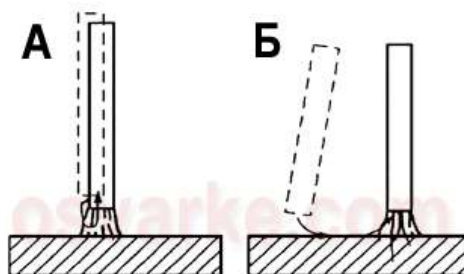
Способы зажигания дуги при ручной дуговой сварке
